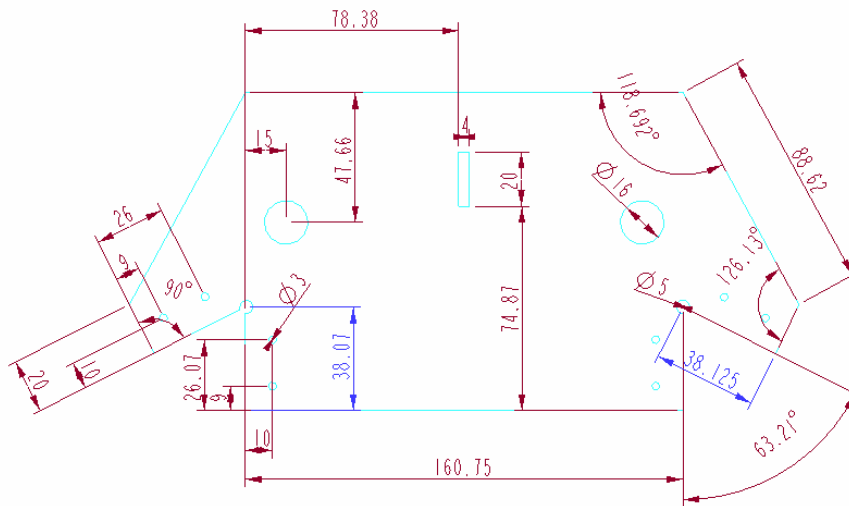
Pieza que muestra la línea de plegado acotada (cota azul)
